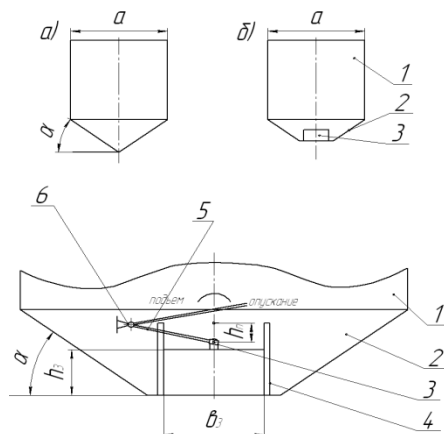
Схема конструкции контейнера-упаковки с боковой разгрузкой (а, б) и схема наклонного затвора с рычажным механизмом открытия и закрытия:
